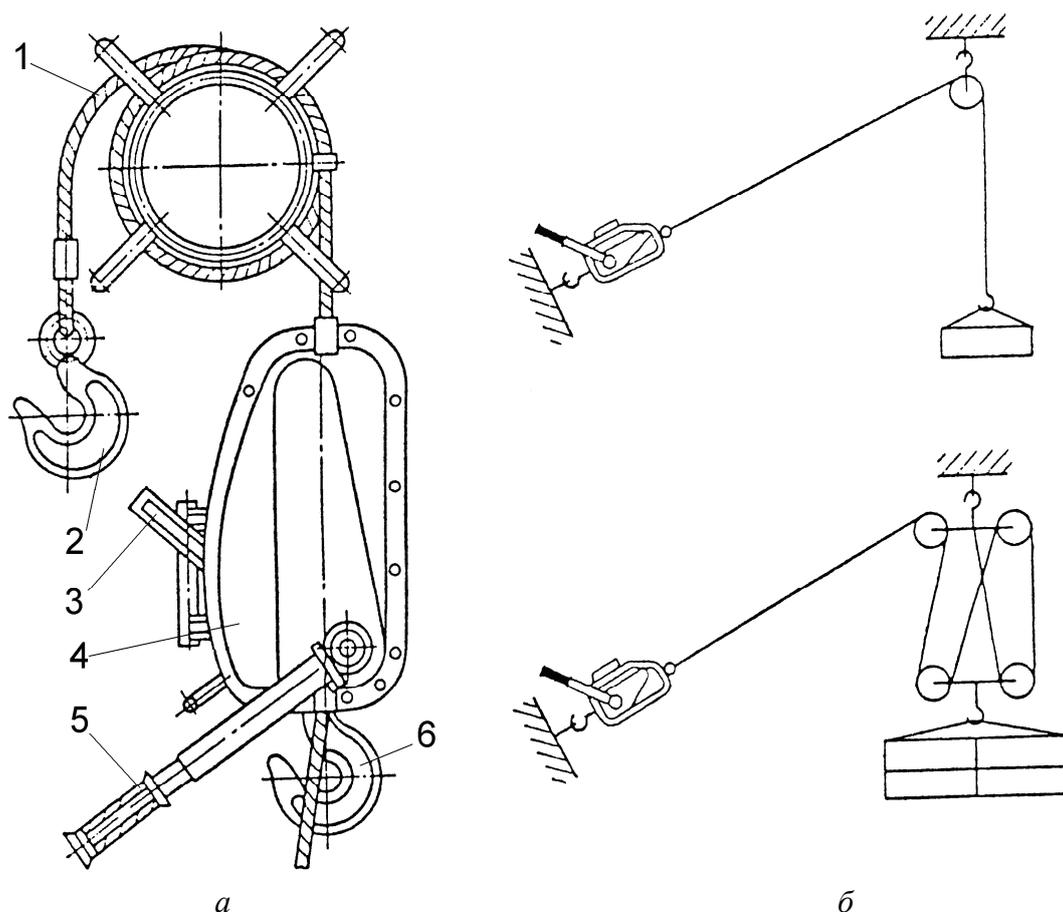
Ручная рычажная лебедка: *а* – общий вид; *б* – схема применения; 1 – канат; 2 – грузовой крюк; 3, 5 – рычаги; 4 – корпус; 6 – крюк для подвески к опоре
